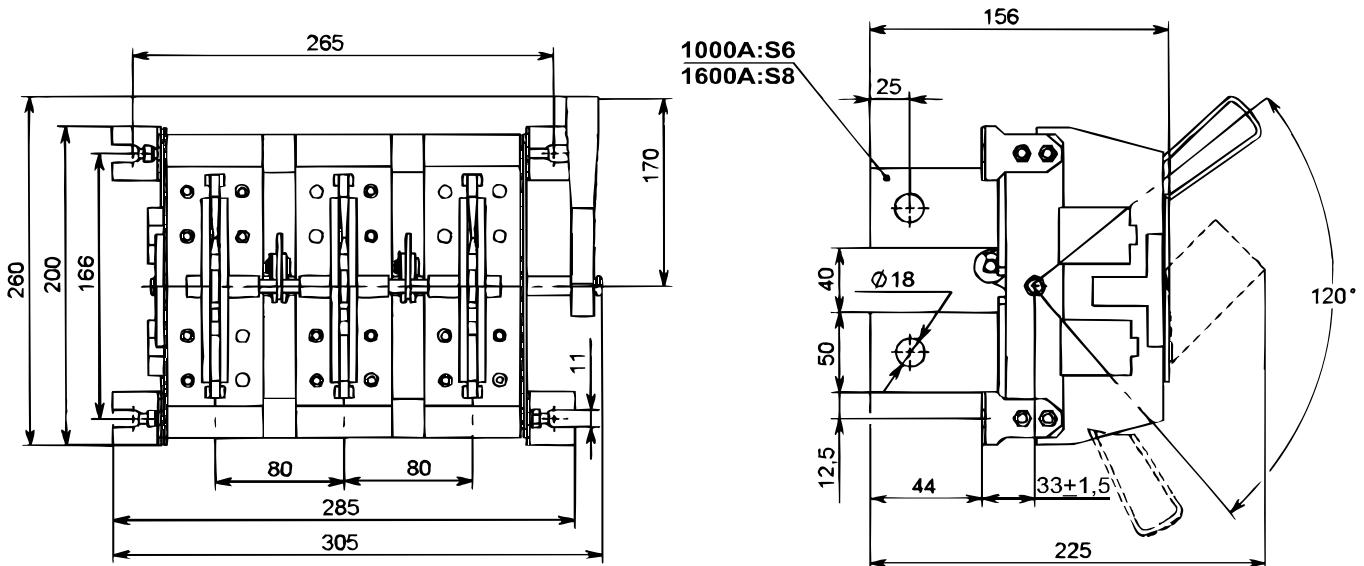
Разъединитель РЕ19-41(43)-32220-00 УХЛЗ с боковой рукояткой, заднего присоединения шин
